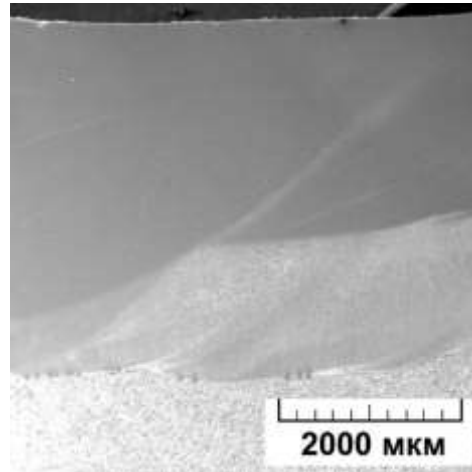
Макрошлиф трехслойной наплавки
